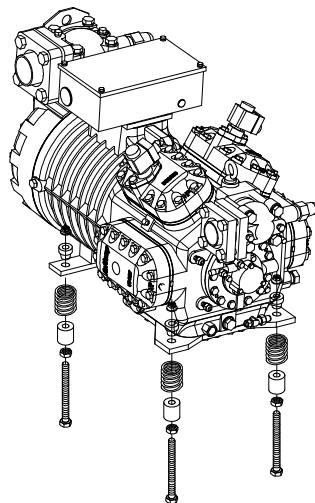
Резиновый демпфер для компрессоров SP8
